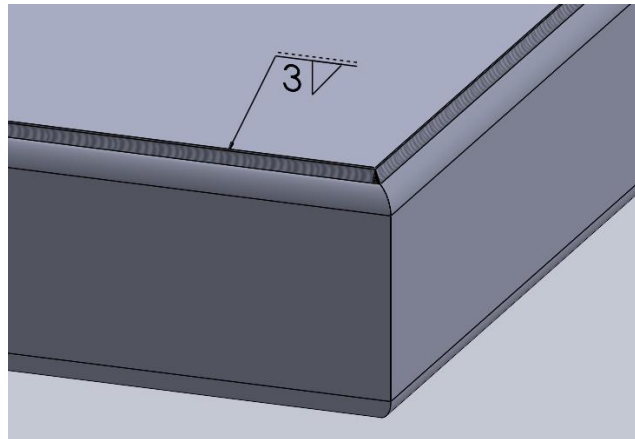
Detalle del modelo CAD del chasis con el cordón de soldadura [fuente propia]
